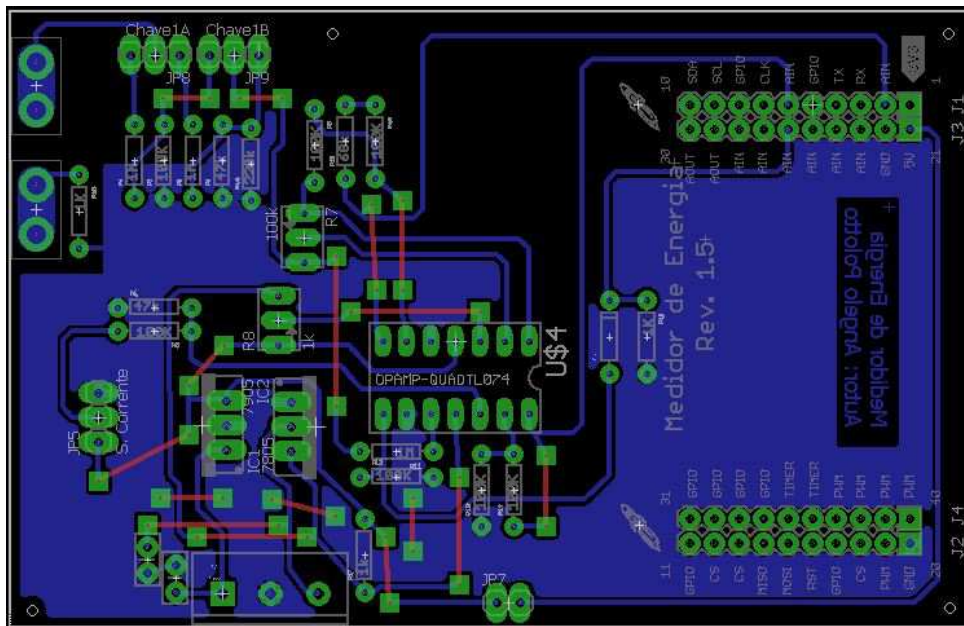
Layout da PCI do Circuito Condicionador de Sinais.
